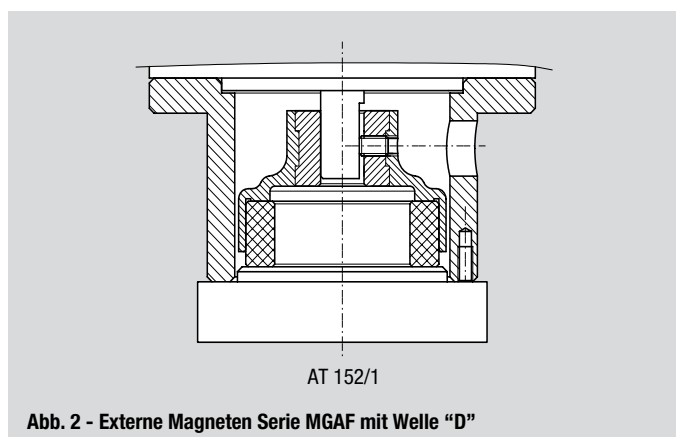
Externe Magneten Serie MGAF mit Welle "D"
